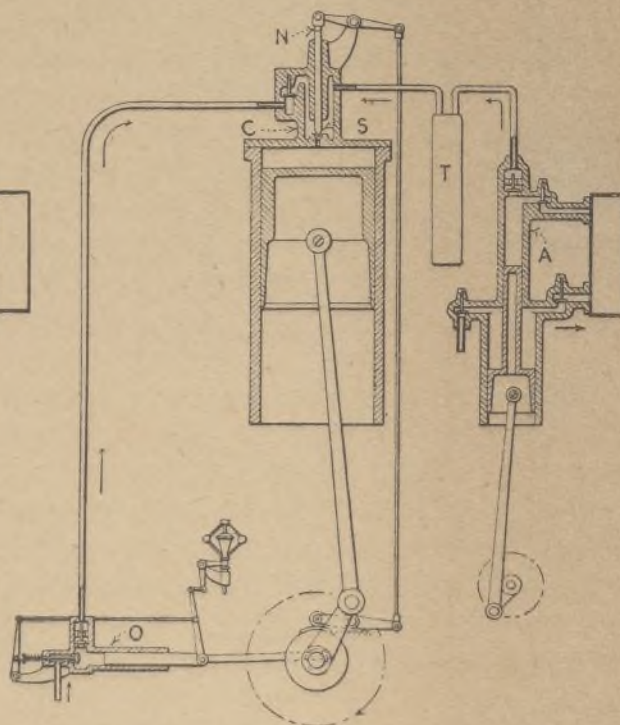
Posición de las piezas de la máquina al iniciarse la entrada del combustible en el cilindro.
